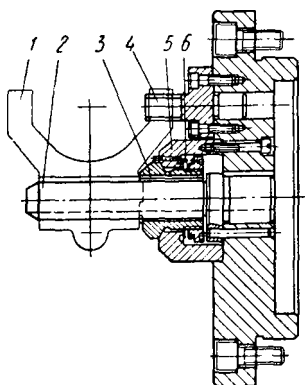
Приспособление для протягивания шпоночного паза в вилках
